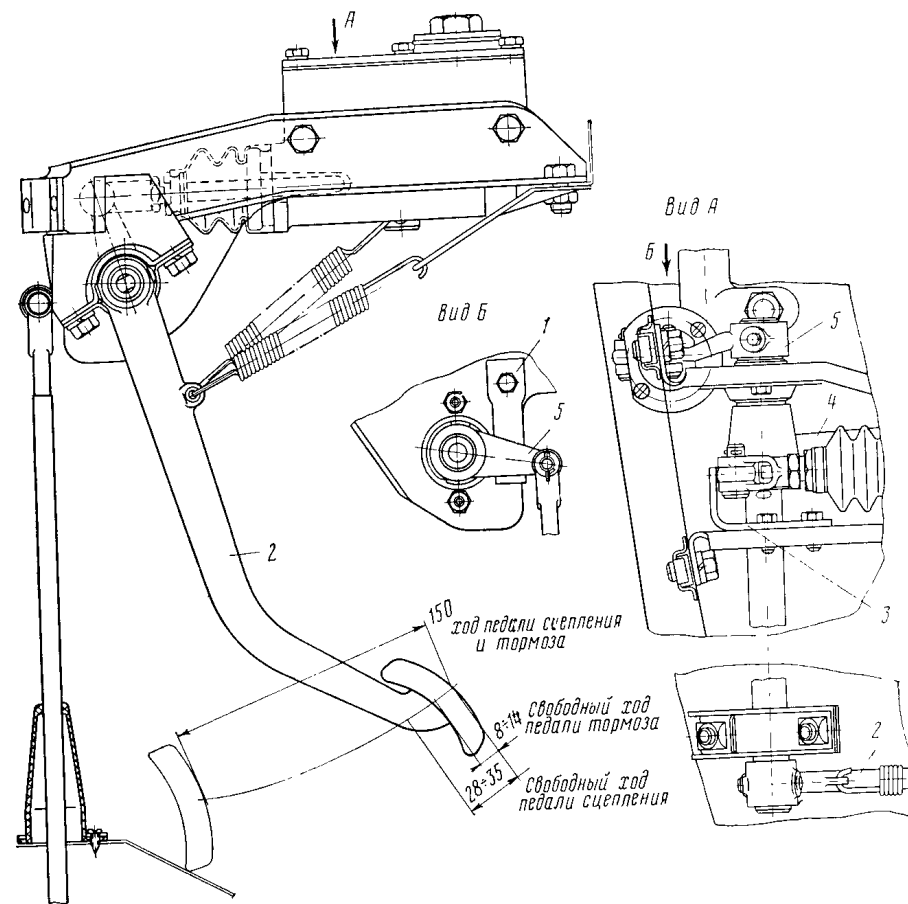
Регулировка положения педалей сцепления и тормоза:
